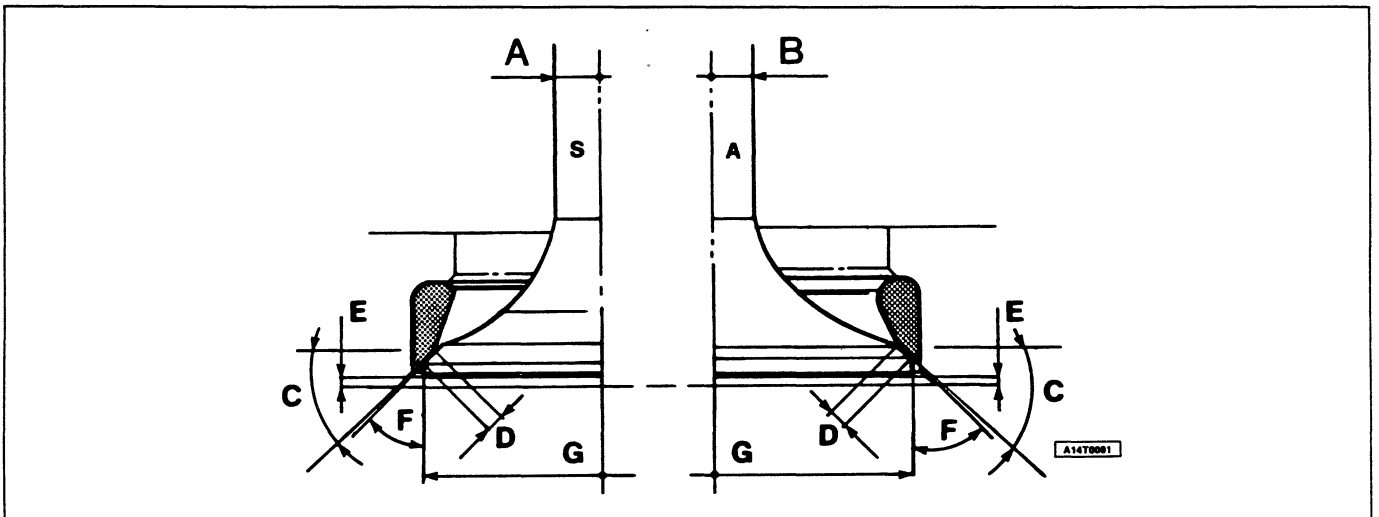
Dimensiones principales de los asientos y de las válvulas.
